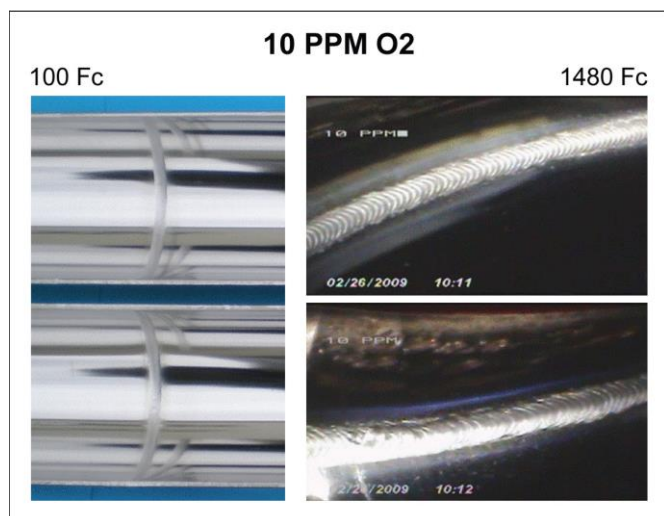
Фотография слева иллюстрирует цвет на сварном шве и в ЗТВ сварного шва, сделанного с 10 ppm O_2 . Крайние фотографии слева показывают изменение цвета сварного шва невооруженным глазом, в то время как на ближайших фотографиях виден тот же сварной шов, что и при использовании бороскопа при мощности 1480 Fc.
